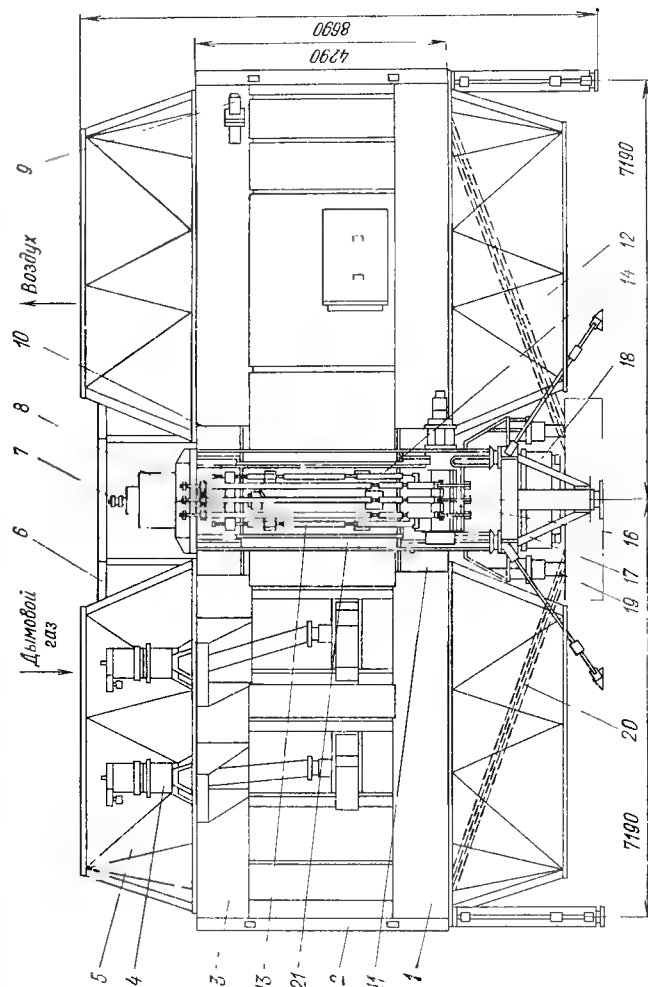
Регенеративный воздухоподогреватель РВП-14,5 (общий вид).
